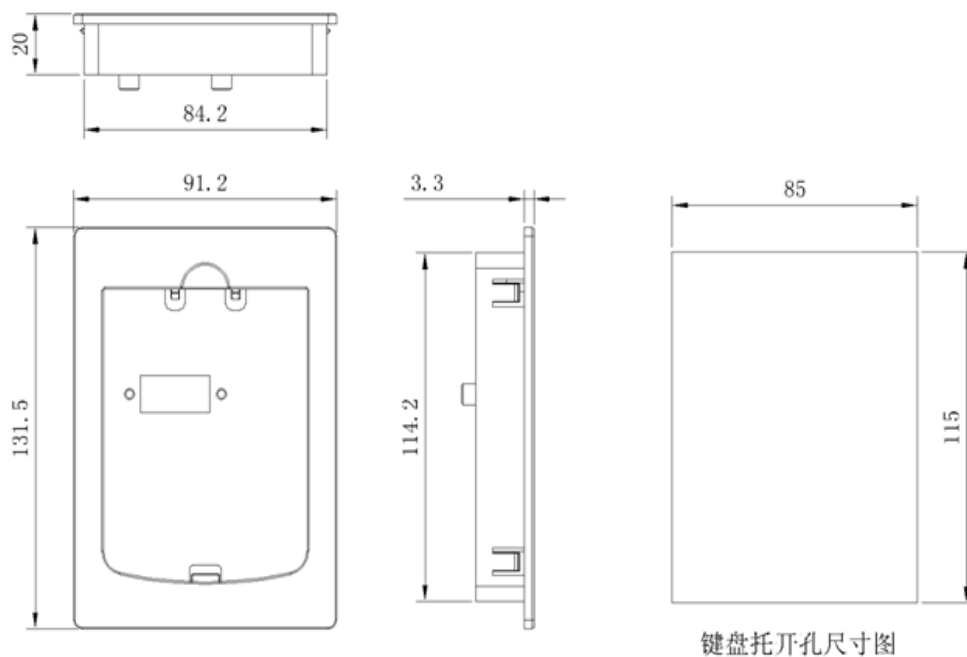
KOC700 系列键盘托的外形及安装开孔尺寸
